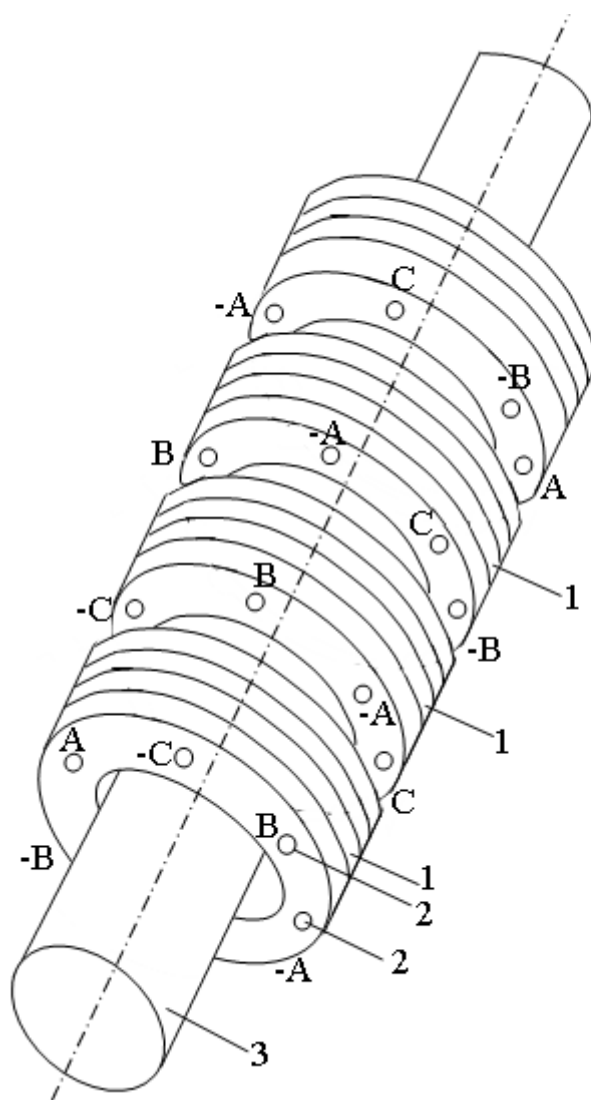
Цилиндрический линейный асинхронный двигатель с вращательно-поступательным перемещением вторичного элемента. 1 – элементарный сердечник индуктора; 2 – трехфазная обмотка; 3 – вторичный элемент
